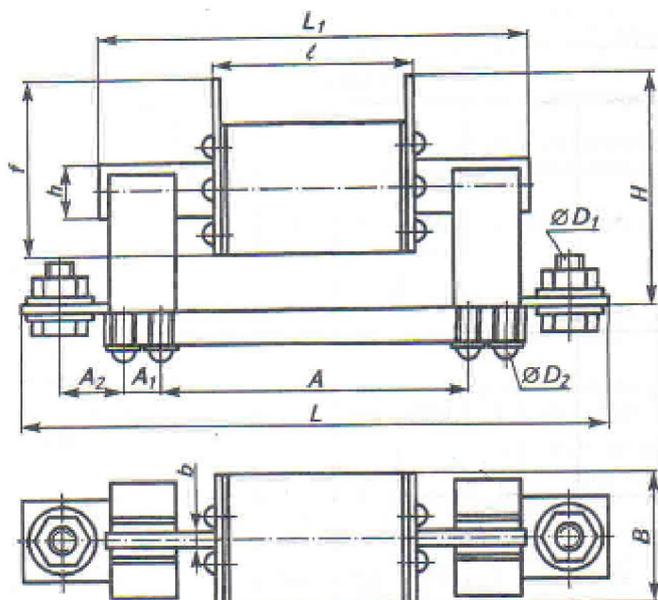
Размеры предохранителя ПН-2 в сборе
